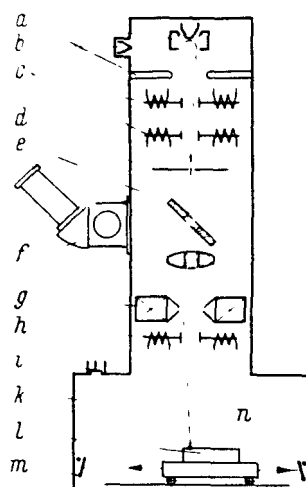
Schema der Elektronenstrahlschweißmaschine [6]
